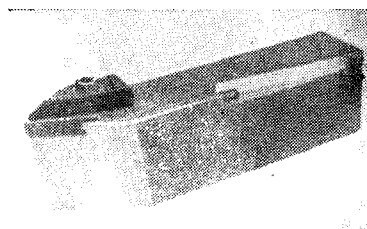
Токарный резец с механическим креплением твердосплавной пластинки для работы на копировальном станке
